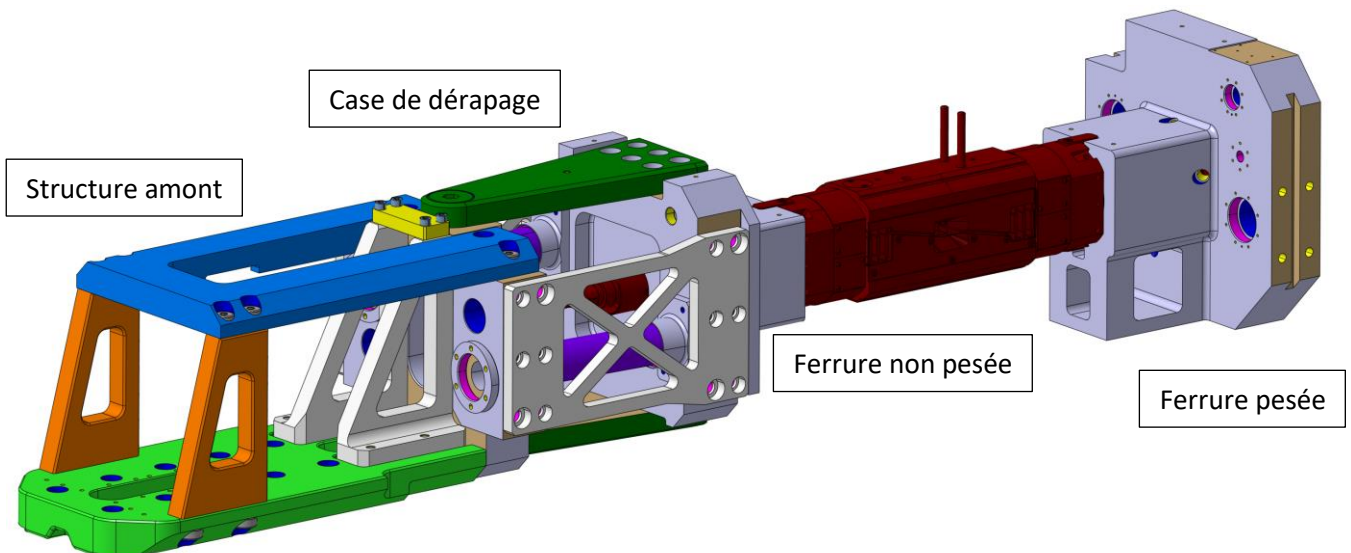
Vue d'ensemble de la structure à fabriquer sans la balance (pièce en rouge)
